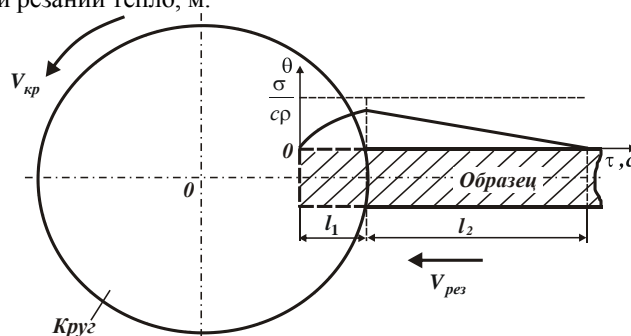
Расчетная схема шлифования прямолинейного образца, движущегося по нормали к рабочей поверхности круга.
